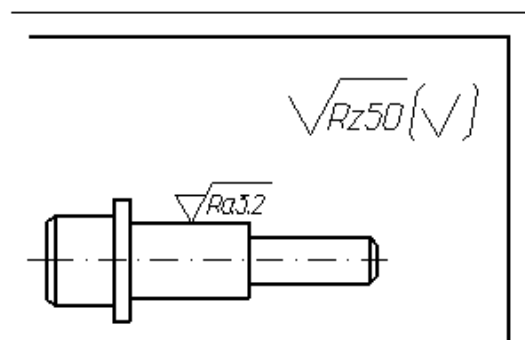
Указание шероховатости одинаковой для части поверхностей изделия
